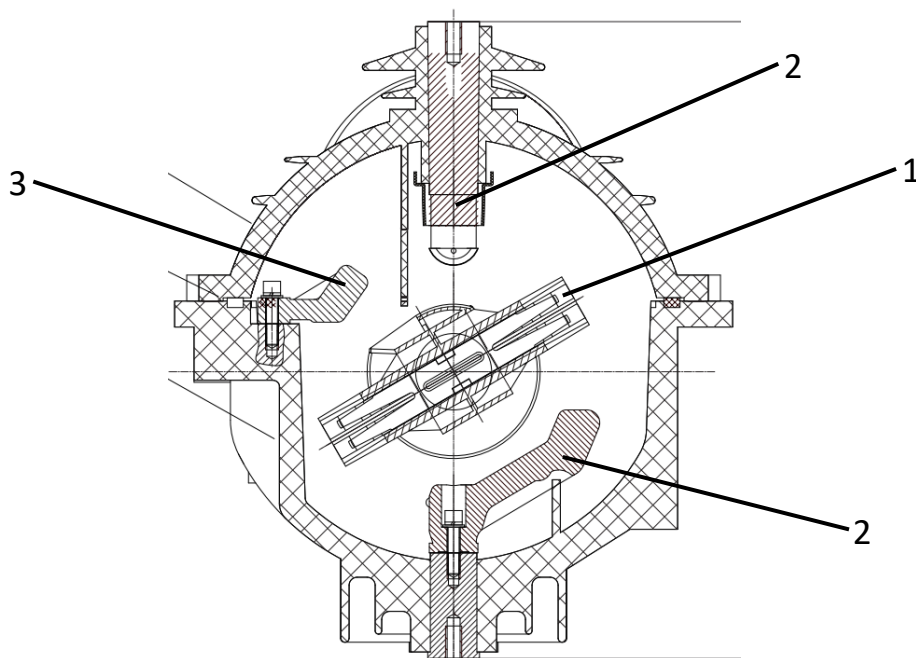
Внутренняя конструкция выключателя нагрузки FLN36-12D
